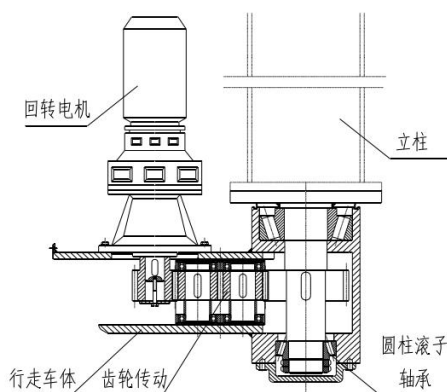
齿轮转动结构原理图 图 (4) 齿轮转动结构实物图
